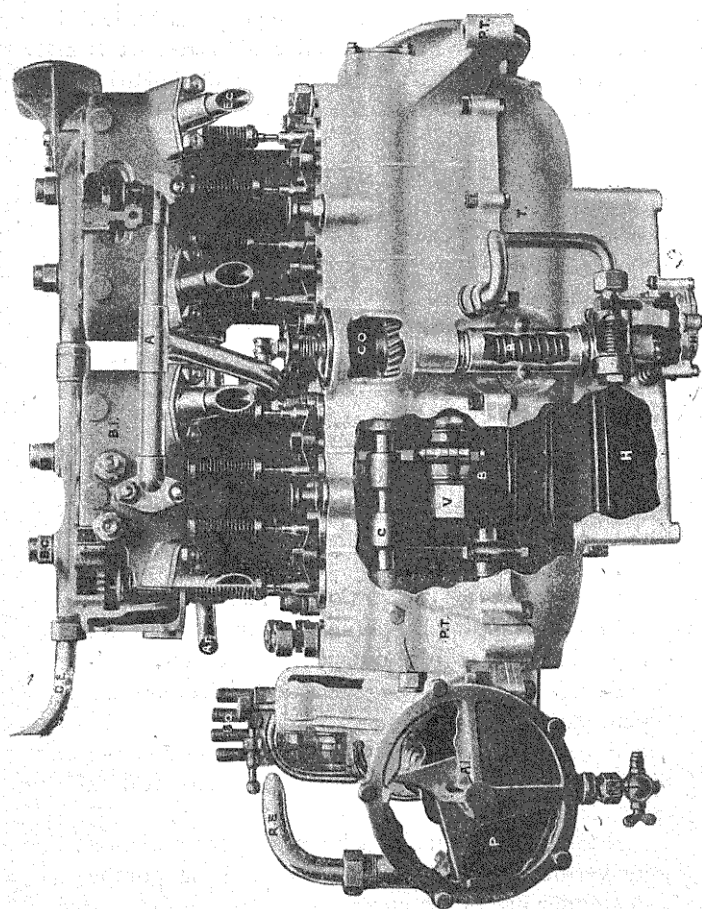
Moteur de Dion 12 chevaux, 4 cylindres 1909 (vue du côté des soupapes). — B C, bouchon de cylindre. — D E, départ de l'eau de refroidissement. — B I, bougie. — A, arrivée d'essence du carburateur. — A R, arrivée d'eau. — E c, échappement. — B O, bornes des fils de bougie. — R E, Tuyau de refoulement de la pompe A i à ailettes P. — C, came commandant les soupapes. — C O, commande de la pompe à huiles P H par l'intermédiaire du ressort R. — V, vilebrequin. — B, bielle. — T, tuyau de refoulement de l'huile. — H, réservoir à huile. — P T, pattes d'attache du moteur au châssis. — R V, robinet de vidange du moteur.
